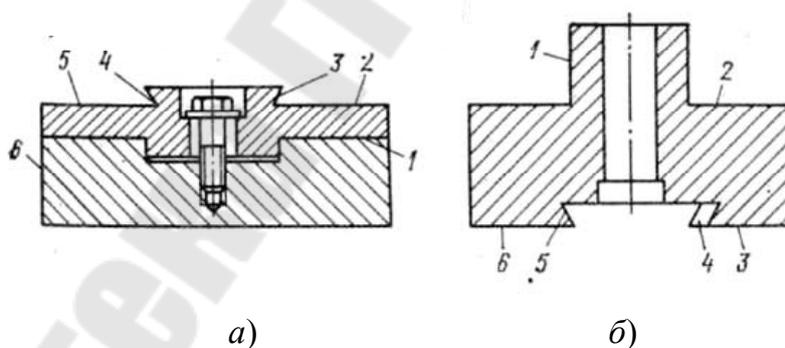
Салазки суппорта: а – поворотные, скрепленные с приспособлениями; б – верхние
